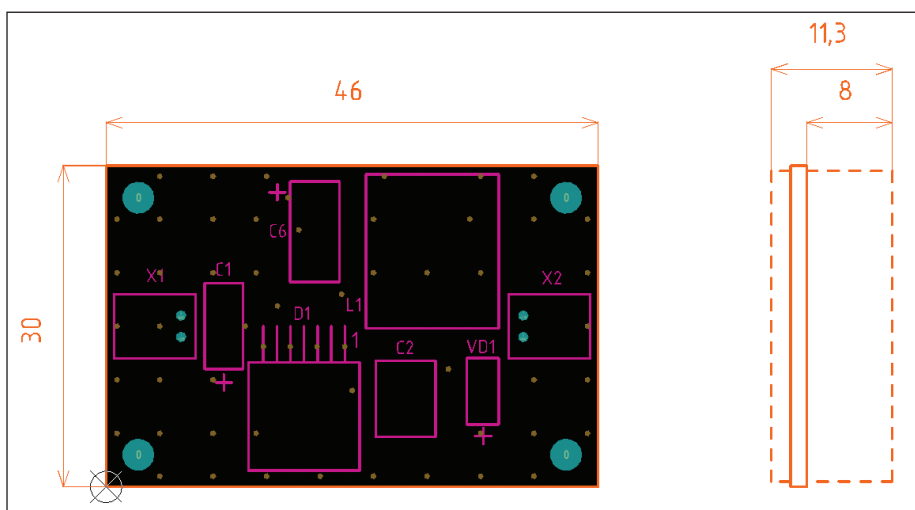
Сформированные в Altium Designer вид сверху и вид сбоку сборочного чертежа
